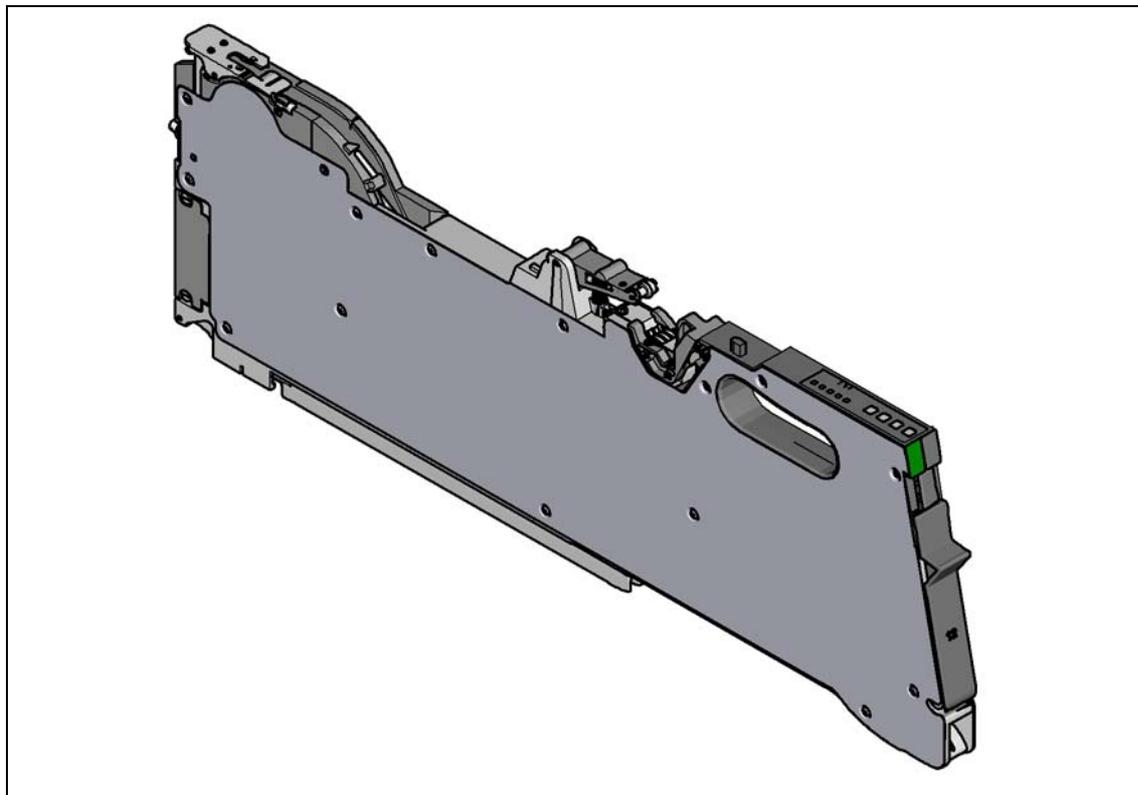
6 8 mm X SIPLACE 智能供料器
